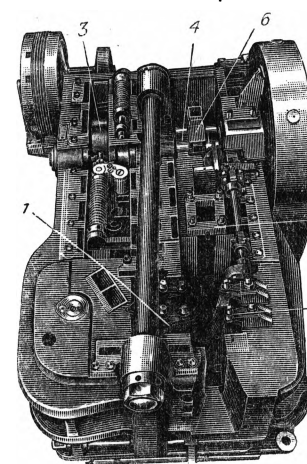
Общий вид горизонтально-ковочной машины: 1—подвижная щечка (матрица), 2—неподвижная щечка (матрица), 3—кулак, приводящий в движение механизм подвижной щечи, 4—коленчатый вал, 5—ползун главный, 6—шатун.
